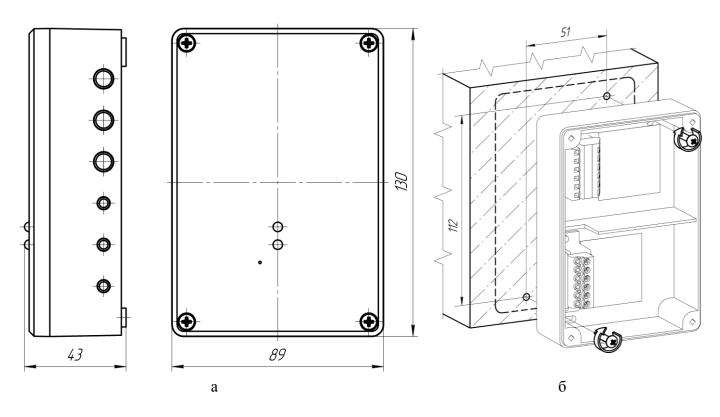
Внешний вид и габаритные размеры (а), установочные размеры (б) блока, размеры в мм.
